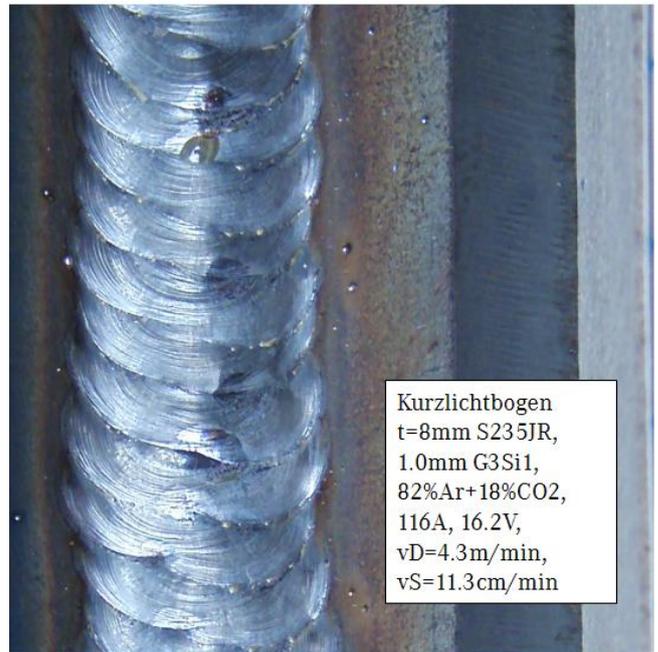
Sehr sorgfältige Steignahtschweißung
